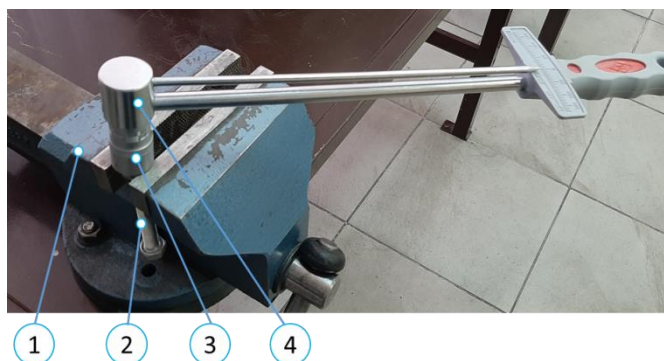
Испытательный стенд для затяжки/откручивания резьбовых соединений с нормированным усилием: 1 – тиски слесарные; 2 – резьбовое соединение «Болт М12 – две гайки»; 3 – головка торцевая; 4 – ключ моментный показывающий КМ-140
